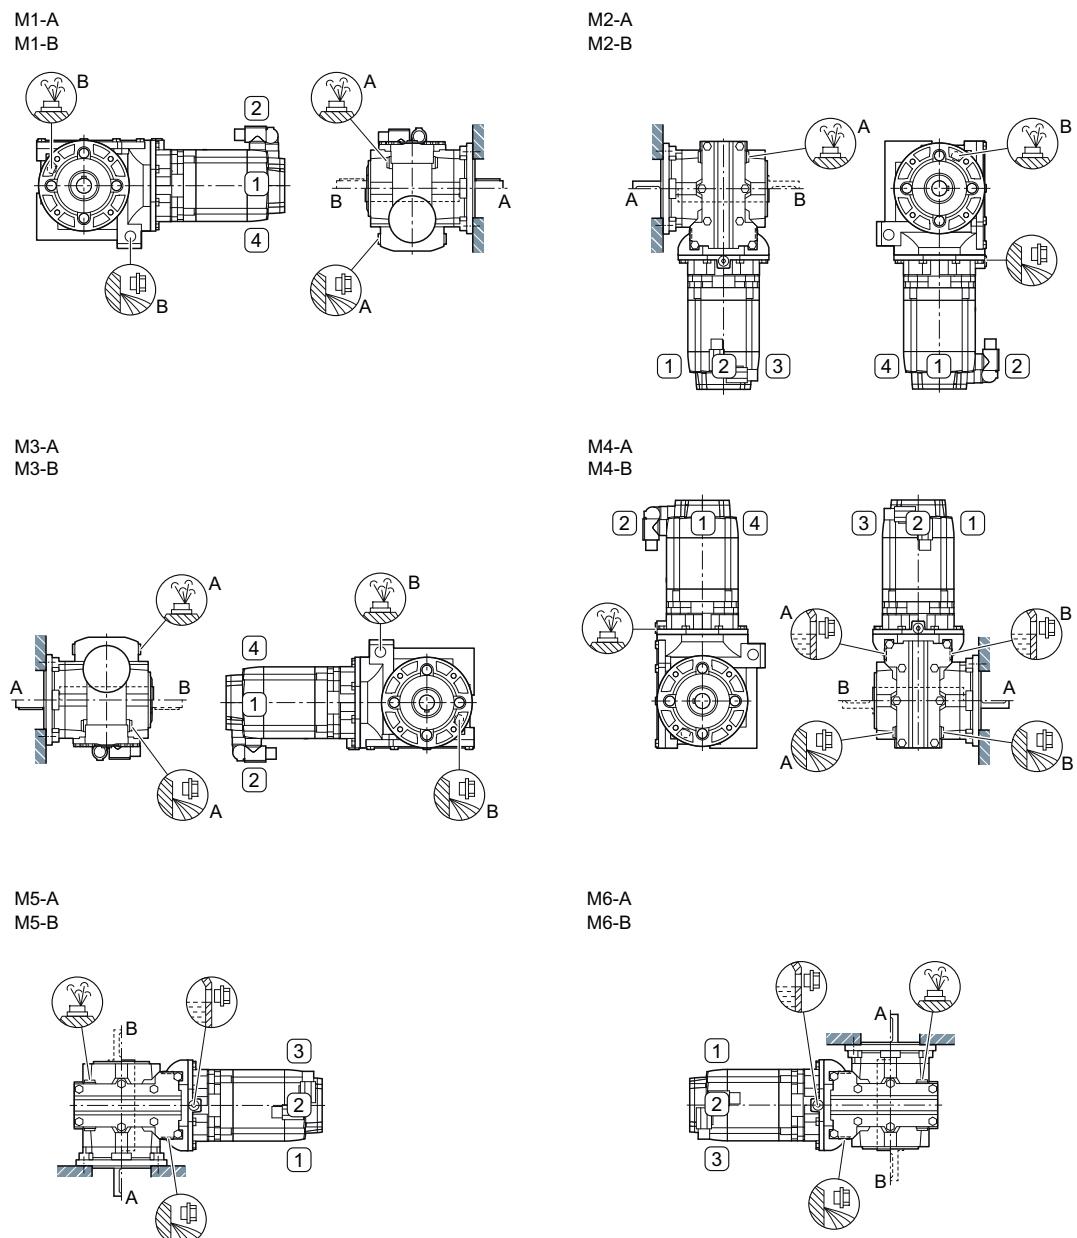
Einbaulagen für Servo-Stirnradschneckengetriebemotor CF (Flanschausführung) und CAZ (Gehäuseflanschausführung), Baugrößen 29, 2-stufig
